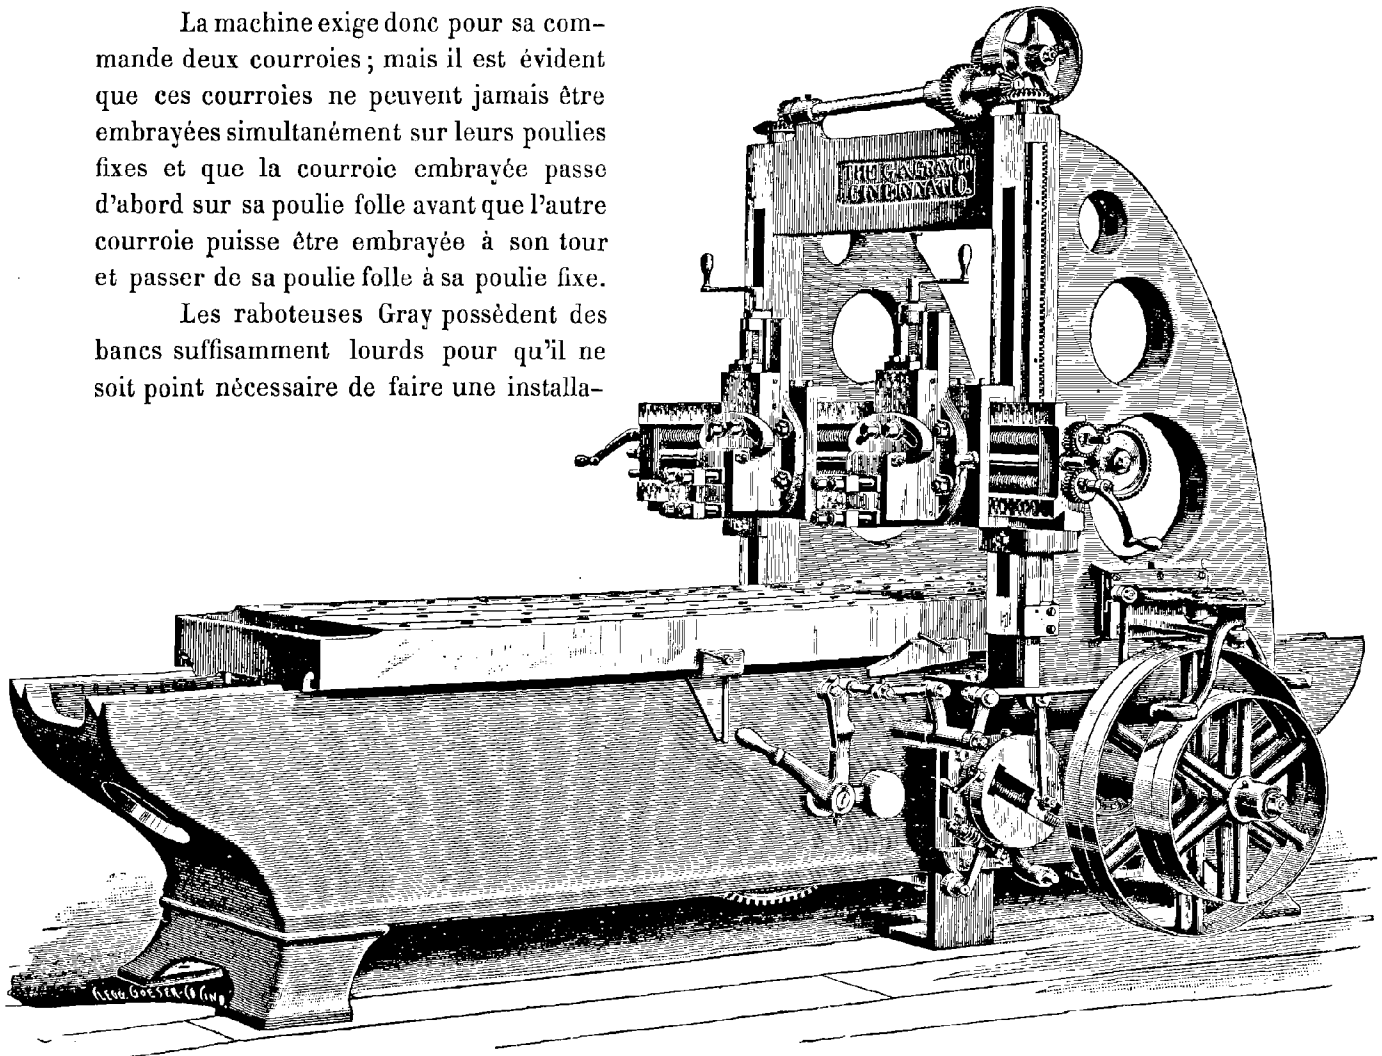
Machine à raboter Gray de la Société Franco-Américaine d'outillage.
